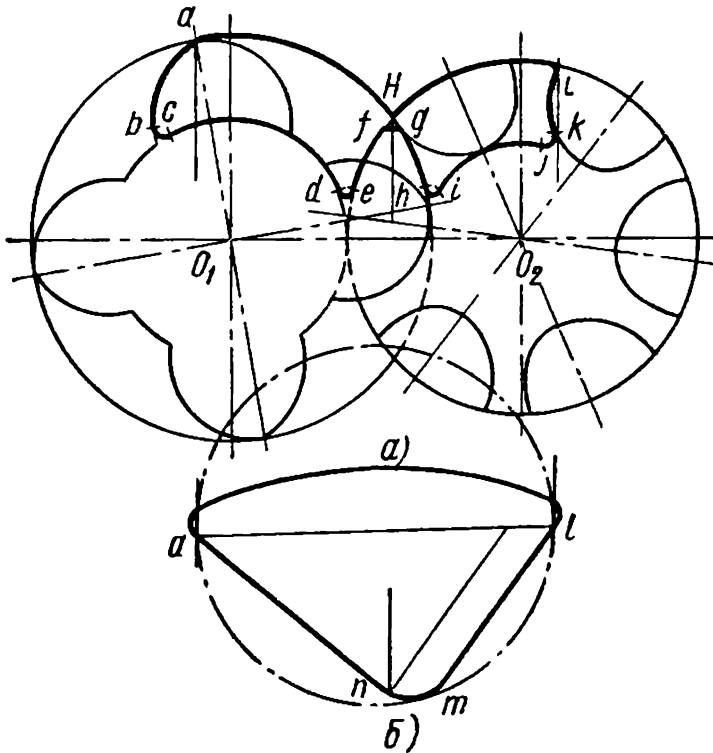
Схема расположения нагнетательного окна винтового компрессора
